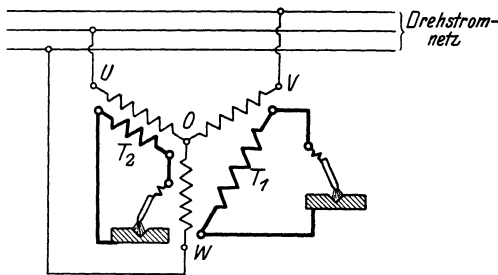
Scottsche Schaltung für Schweißumspanner.
